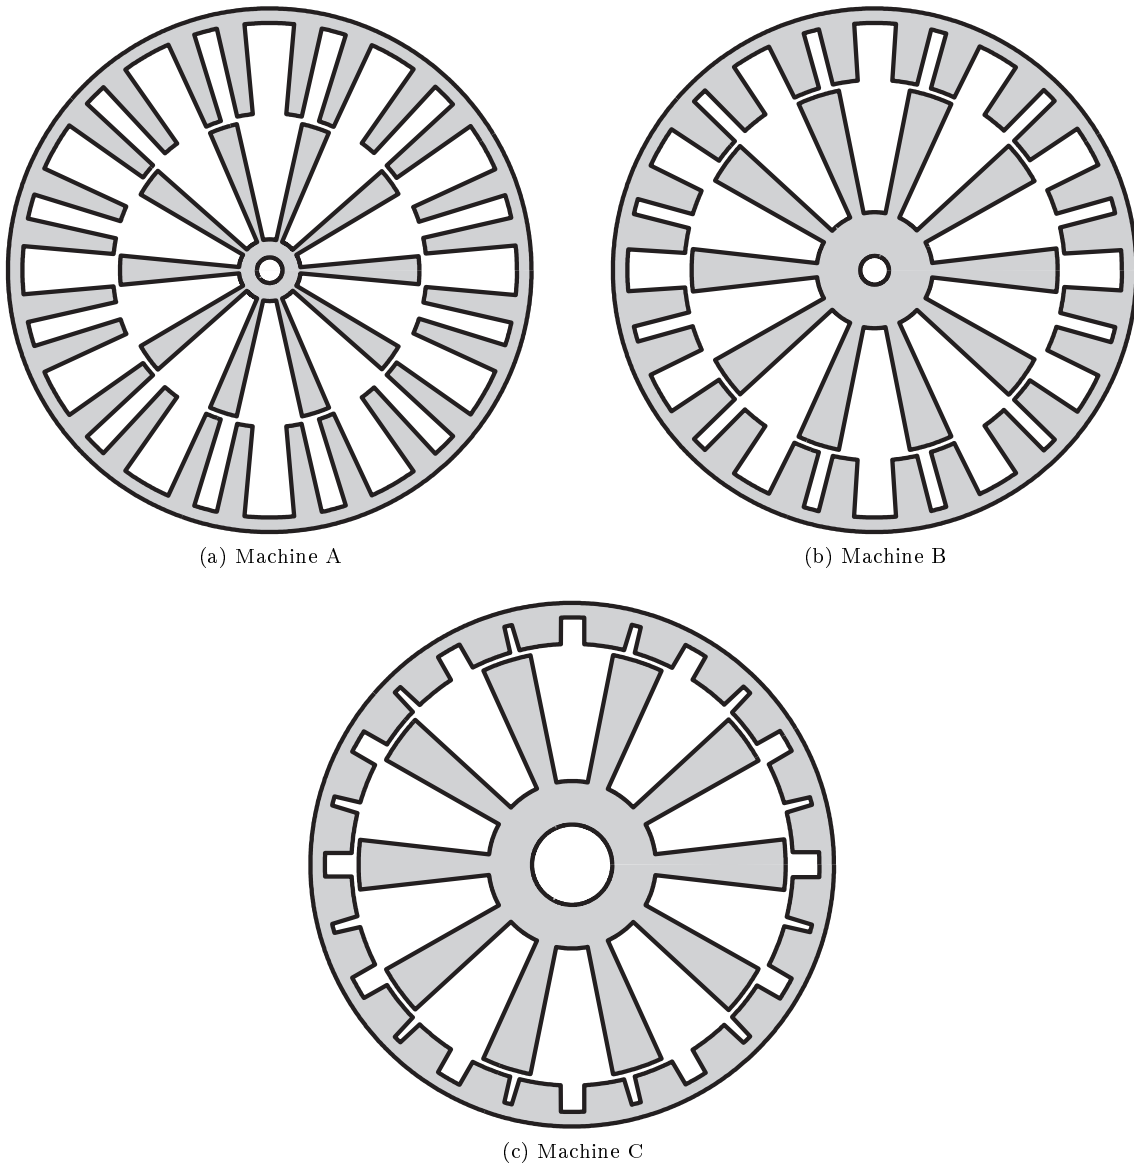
Coupes transversales des machines A, B et C - Structure 24-10
